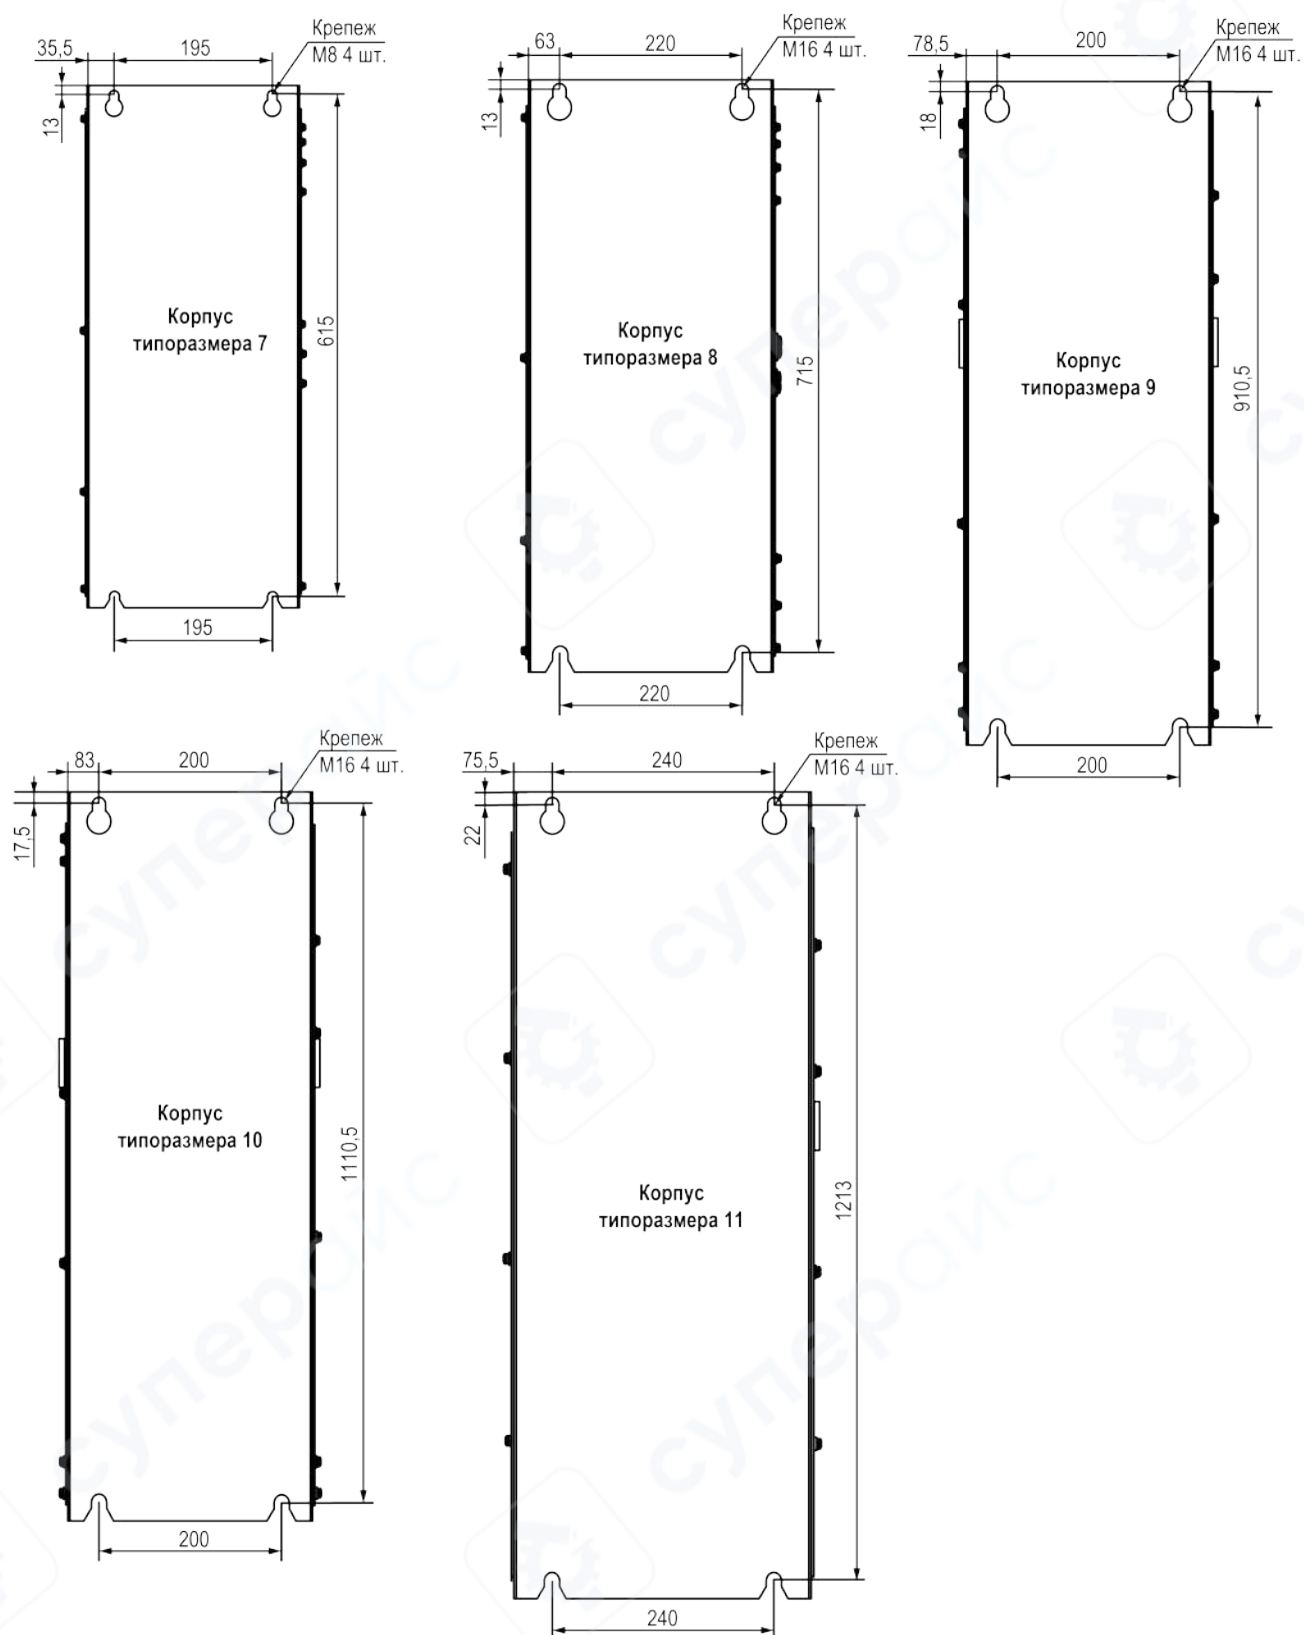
Присоединительные размеры для корпусов типоразмеров 7–11
